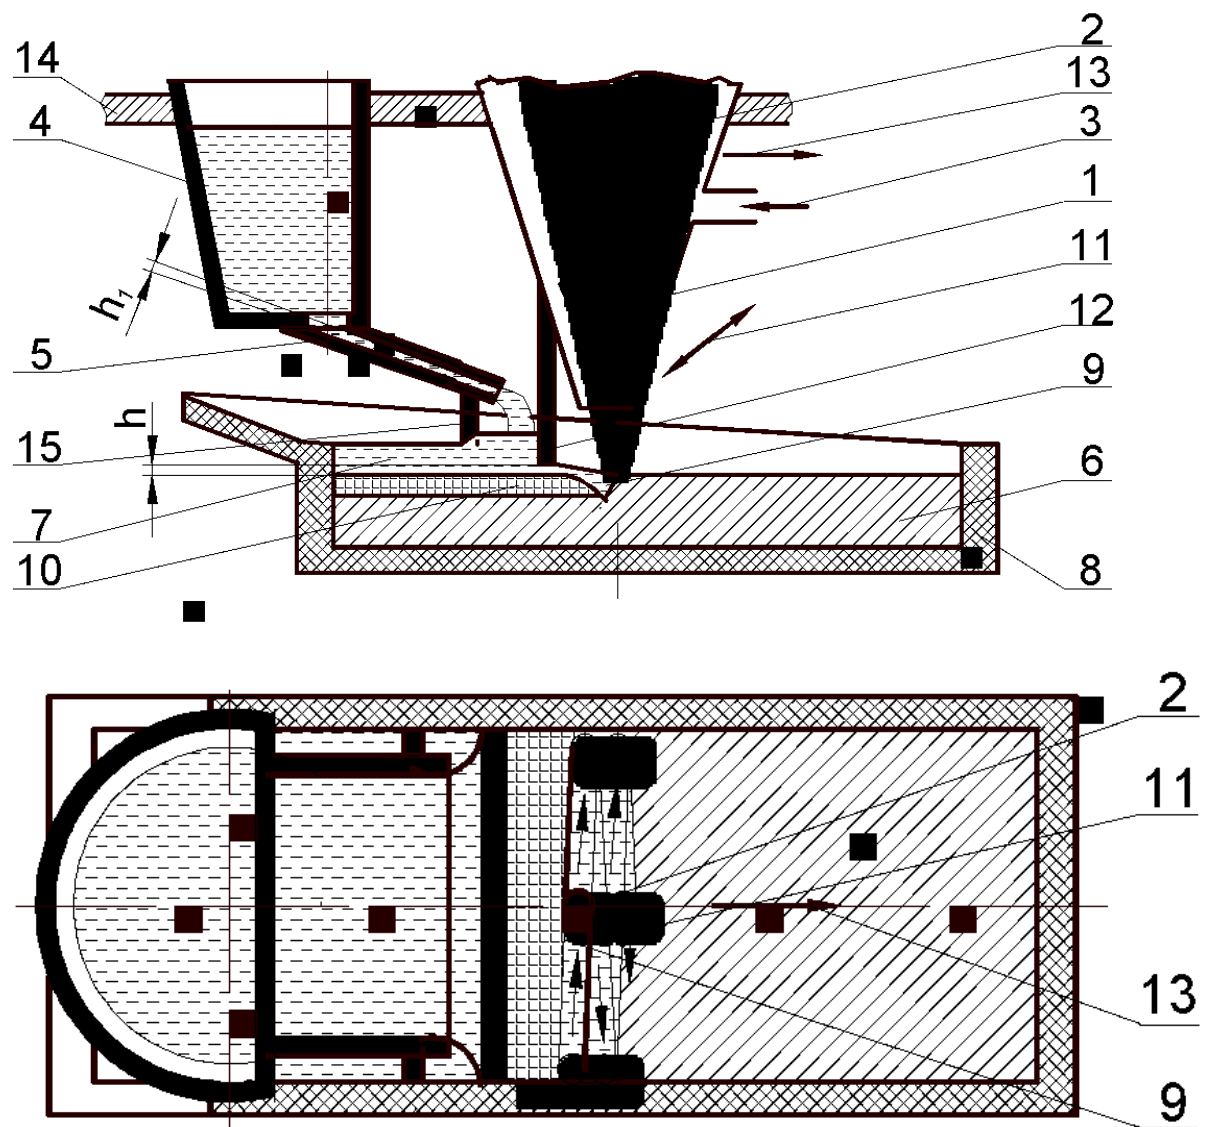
Пристрій для лазерно-ливарного виготовлення біметалів
